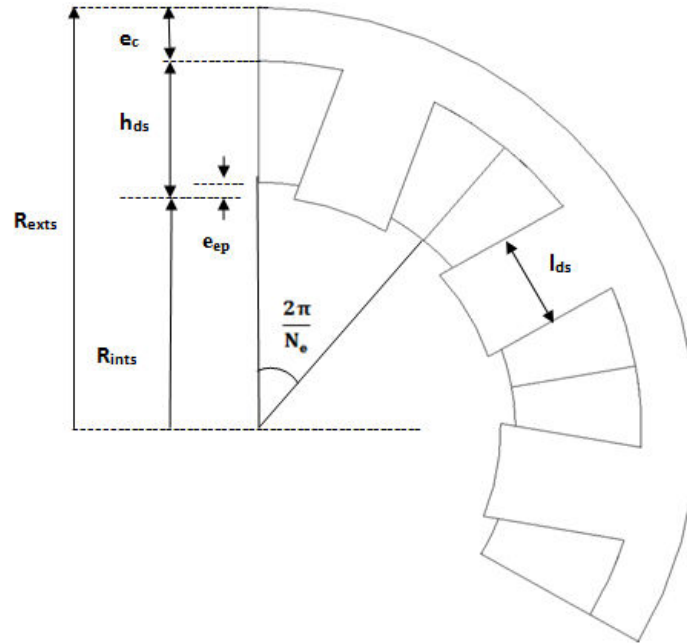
Dimensions géométriques du stator des machines étudiées.
